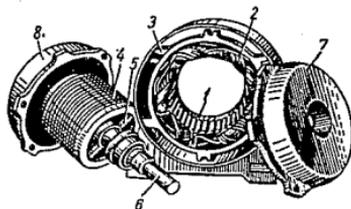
Motor asincrónico con rotor de jaula de ardilla desarmado
